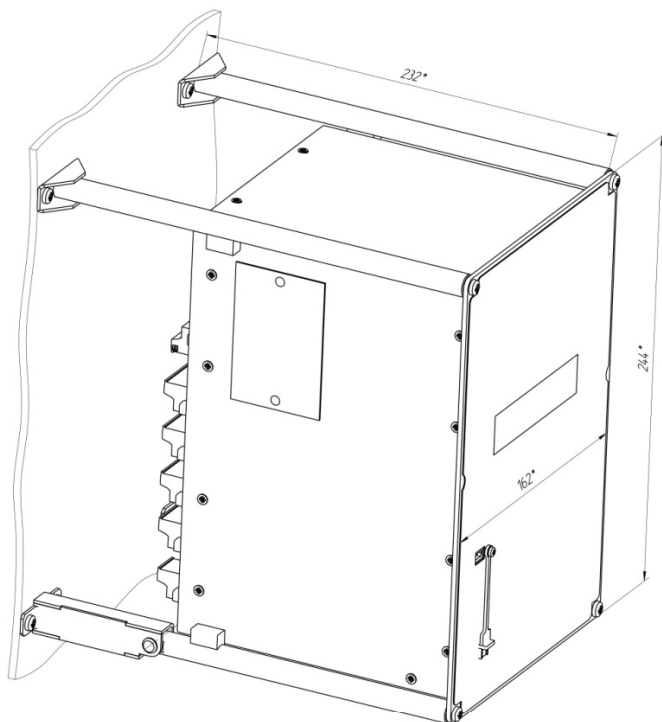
Габаритные и присоединительные размеры устройства РС830-М2 при внешнем монтаже, обеспечивающем его поворот влево/вправо
